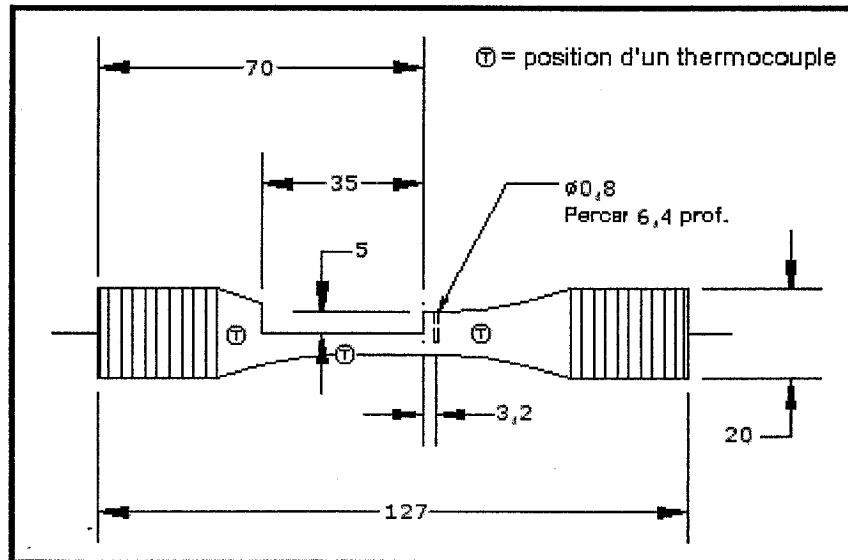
Dessin technique de l'éprouvette utilisée pour mesurer le coefficient d'émissivité de l'acier ASTM A516
